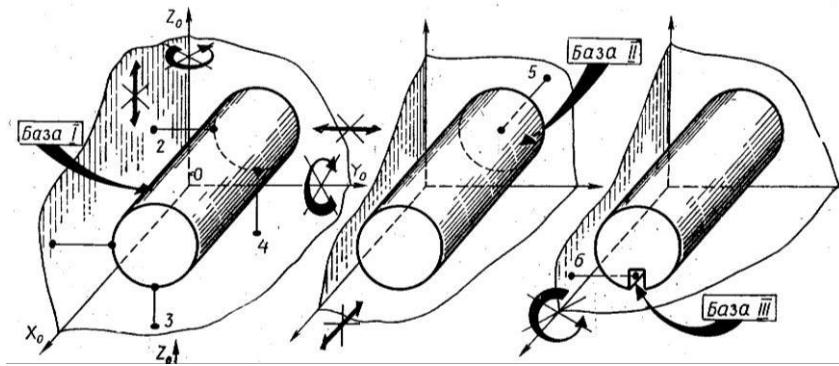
Базування довгого циліндричного тіла [3]
